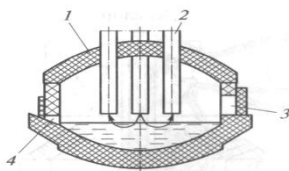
Схема дуговой сталеплавильной печи (ДСП):
